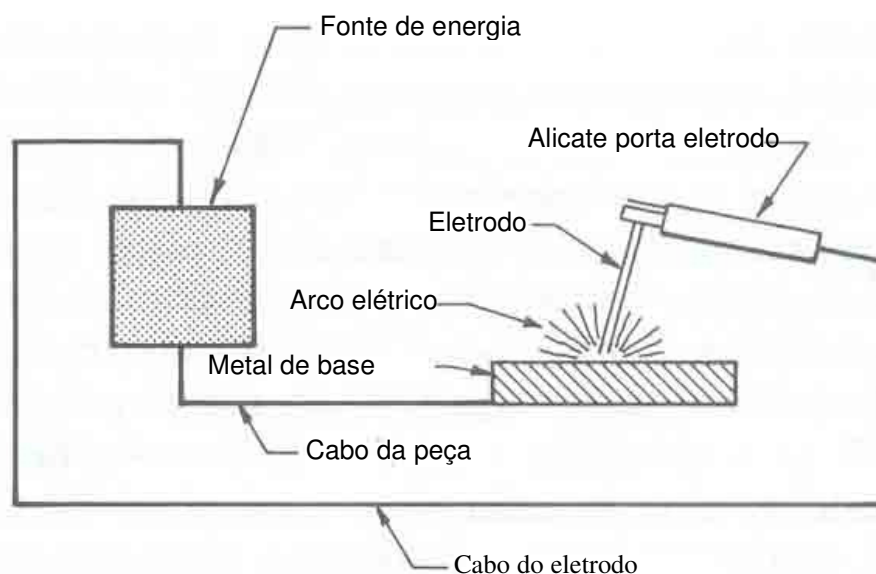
Equipamento básico para soldagem a arco elétrico (The James F. Lincoln Welding Foundation, 2000)
